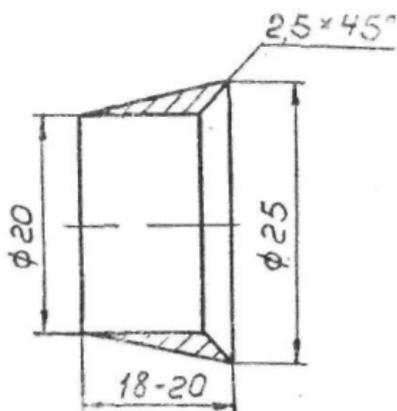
Конусная втулка для установки полуоси коленчатого вала в сальник.
